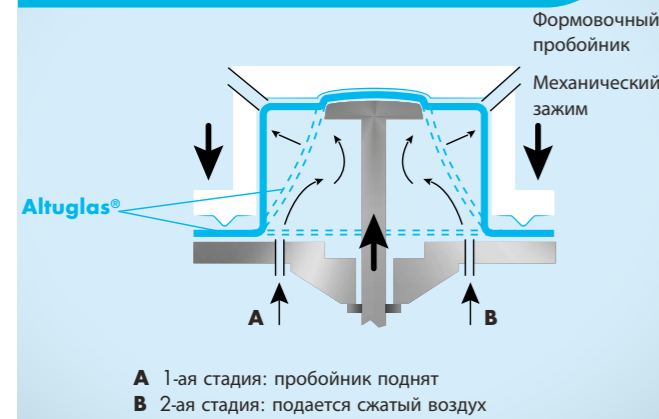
Формовка вакуумной вытяжкой и прессованием
